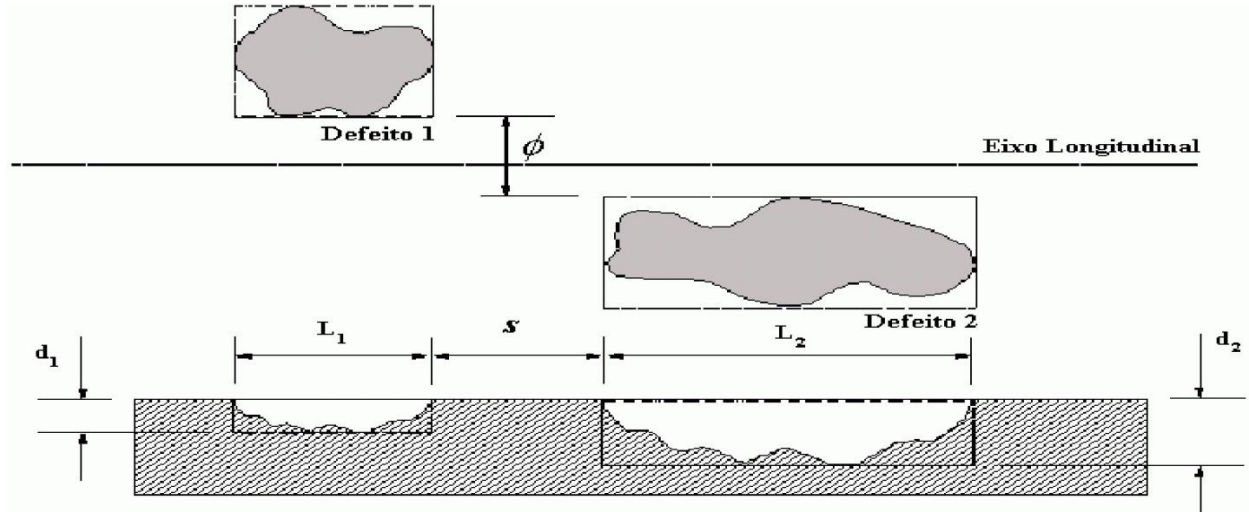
Dimensionnement Des Défauts Des Pic De Corrosion [7]
